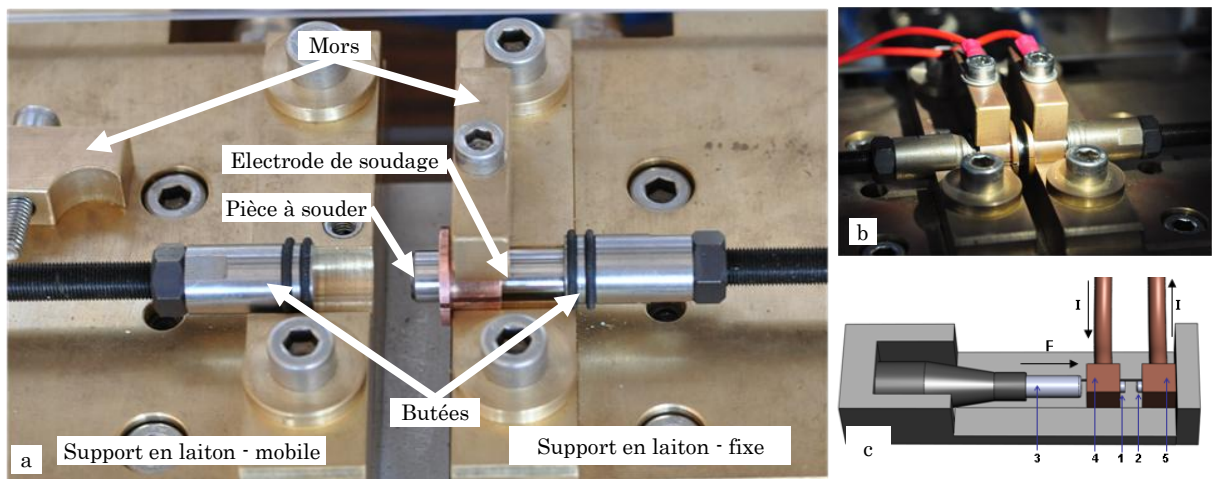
Tête de soudage de l'installation SOPRANO a : hors position de soudage, b : en position de soudage, c : vue schématique
